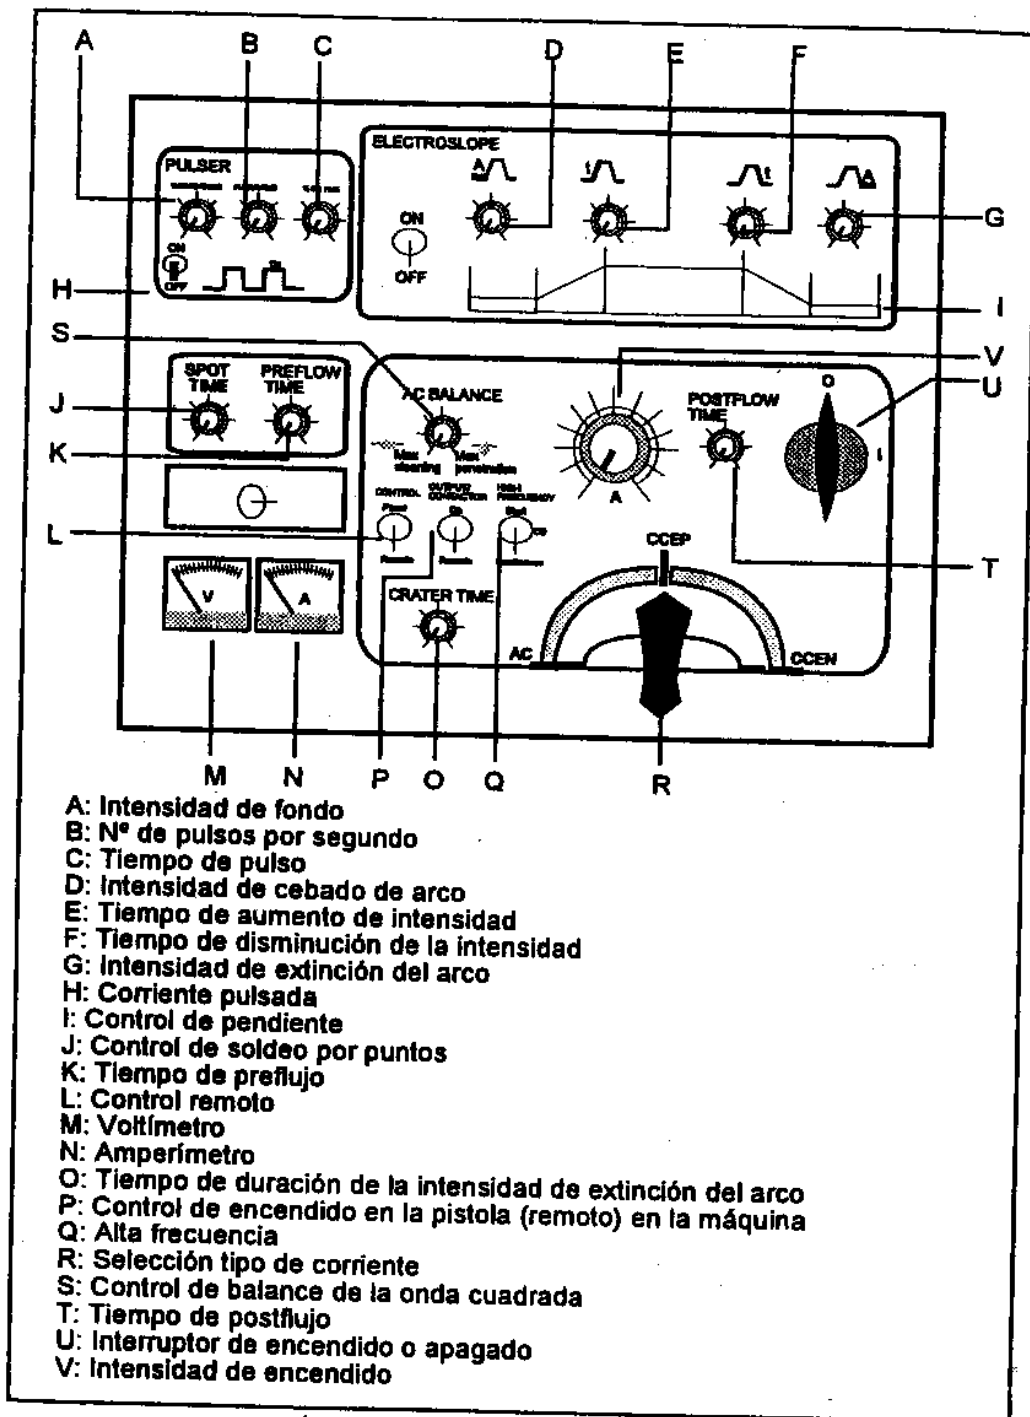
PANEL DE CONTROL DE UNA MÁQUINA TIG
